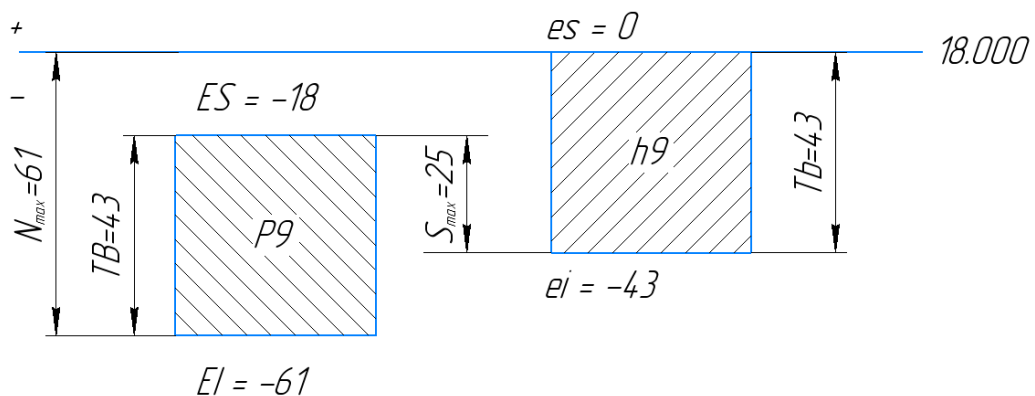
Схема полів допусків з'єднання вал-шпонка
